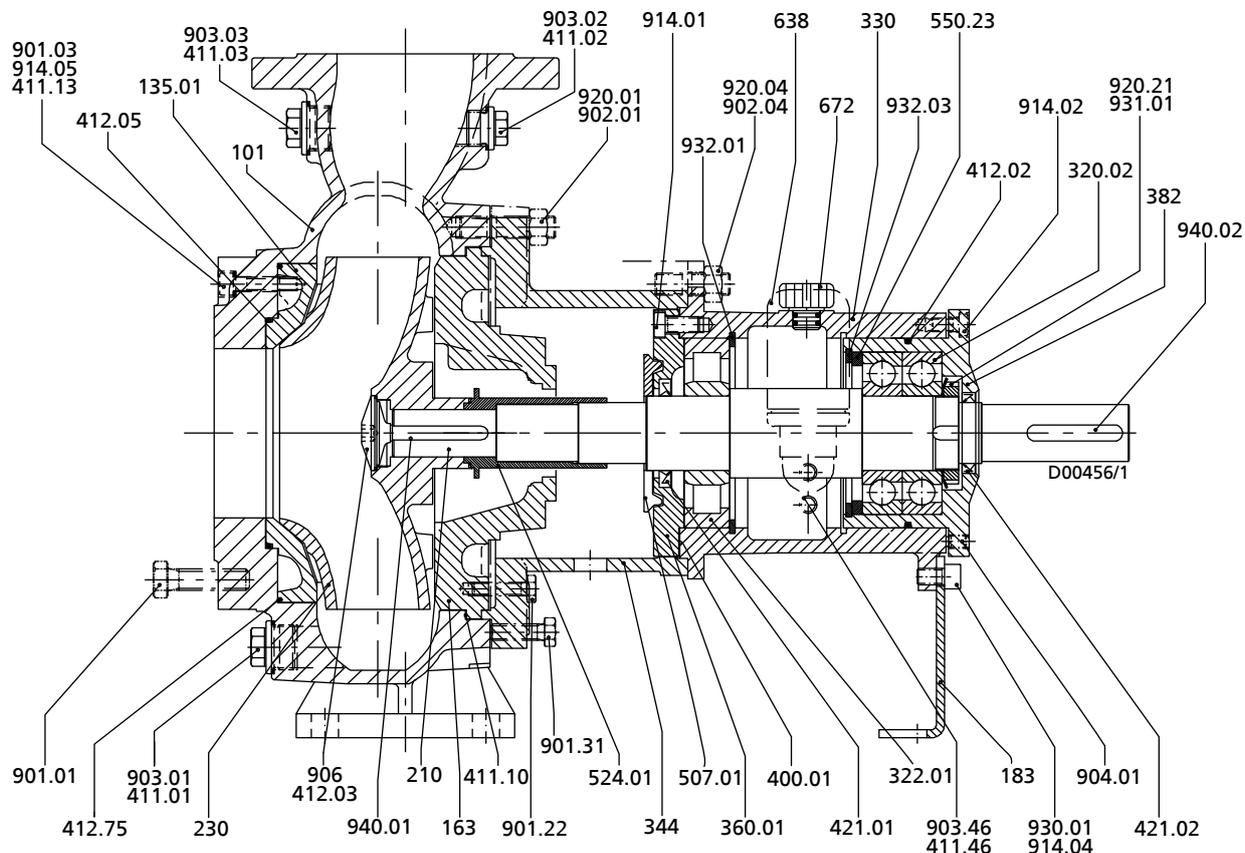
Сборочный чертеж насоса с подшипниковым кронштейном с P03ах по P06х
